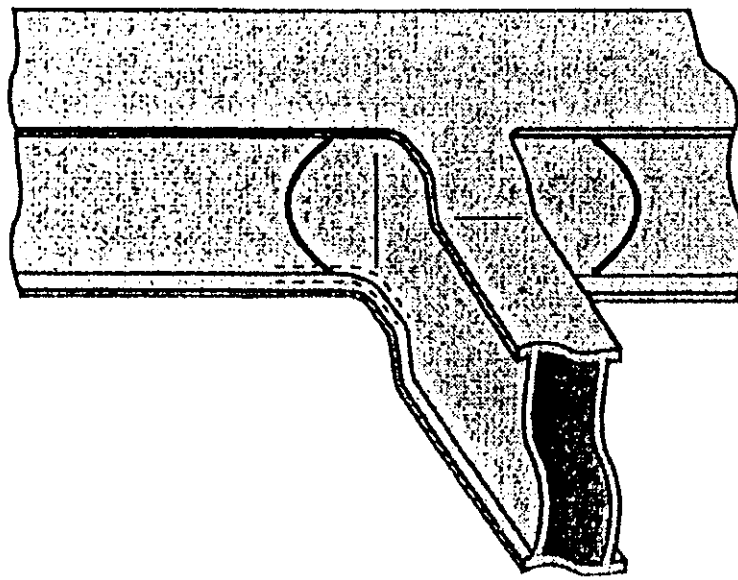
Контроль сварных швов соединения верхних и нижних стенок с боковыми стенками
